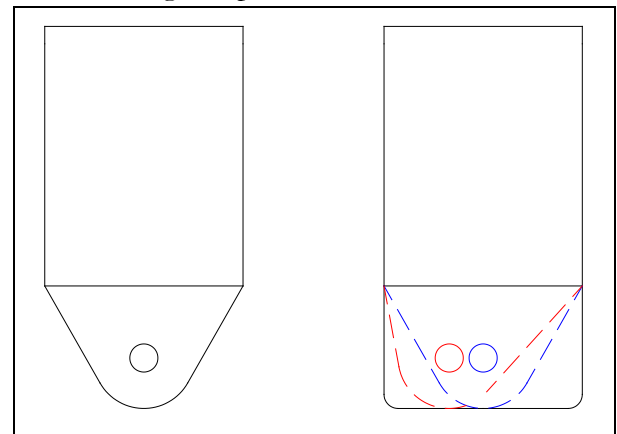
Izquierda: geometría proyectada. Derecha: geometría construida.
